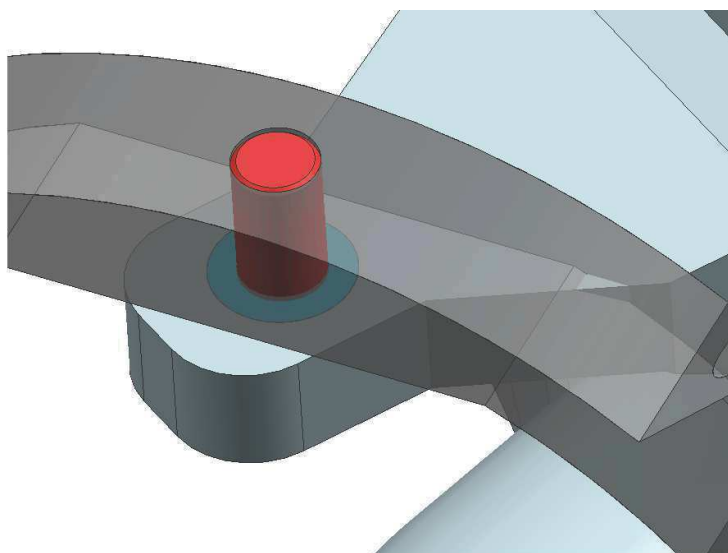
Objímka spojující přední a zadní část manipulátoru.
